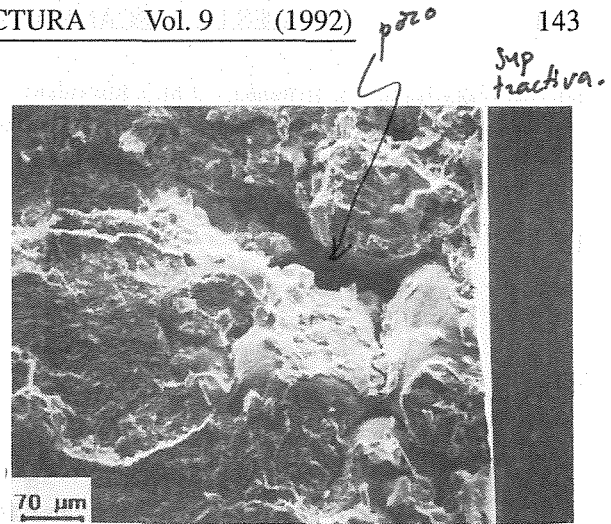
Inicio de la fractura. Px30S sinterizado en vacío y revenido a 535 °C.
